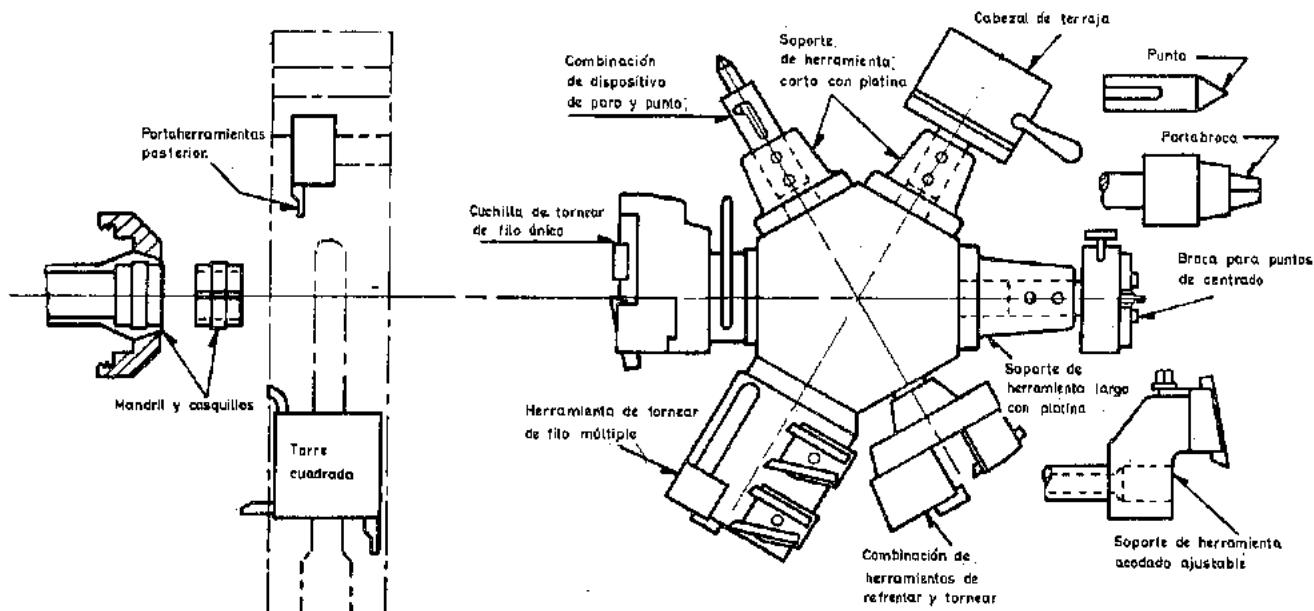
Montaje permanente del equipo universal para trabajos sobre barra (Warner & Swasey Co.)
